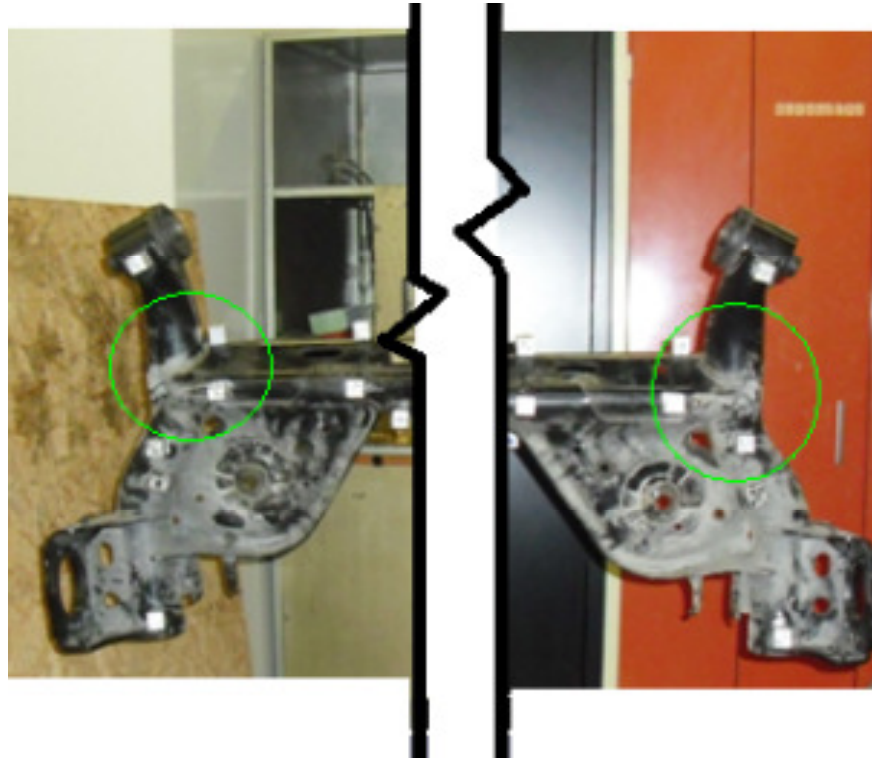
14-- Identificação cordões de soldadura ligação barra central restante corpo.
